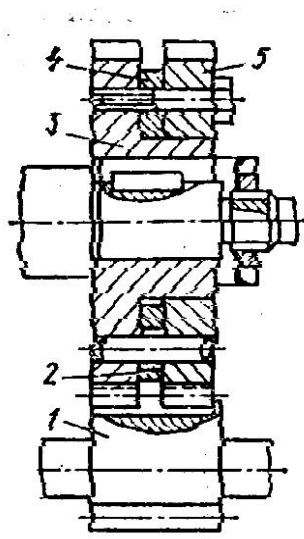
Схема усунення зазору в редукторі поперечної подачі верстата
